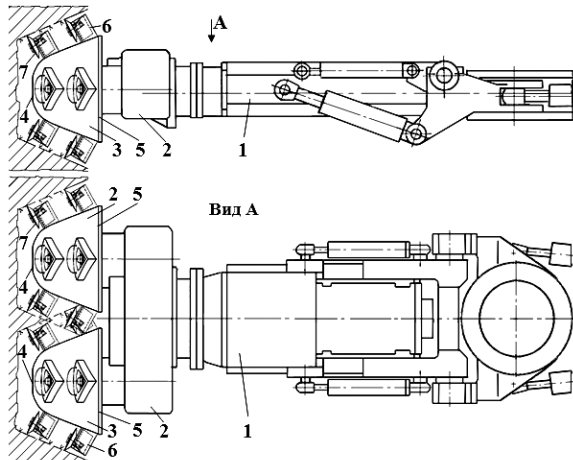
Двухкорончатый реверсивный исполнительный орган с дисковым инструментом
